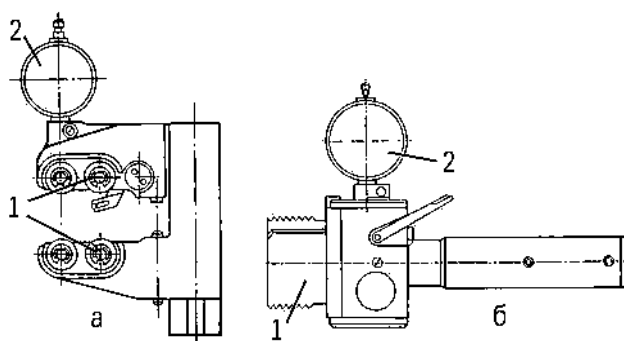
Схемы индикаторных приборов для измерения наружной (*a*) и внутренней (*б*) резьб: 1 – резьбовые измерительные элементы; 2 – отсчетное устройство
